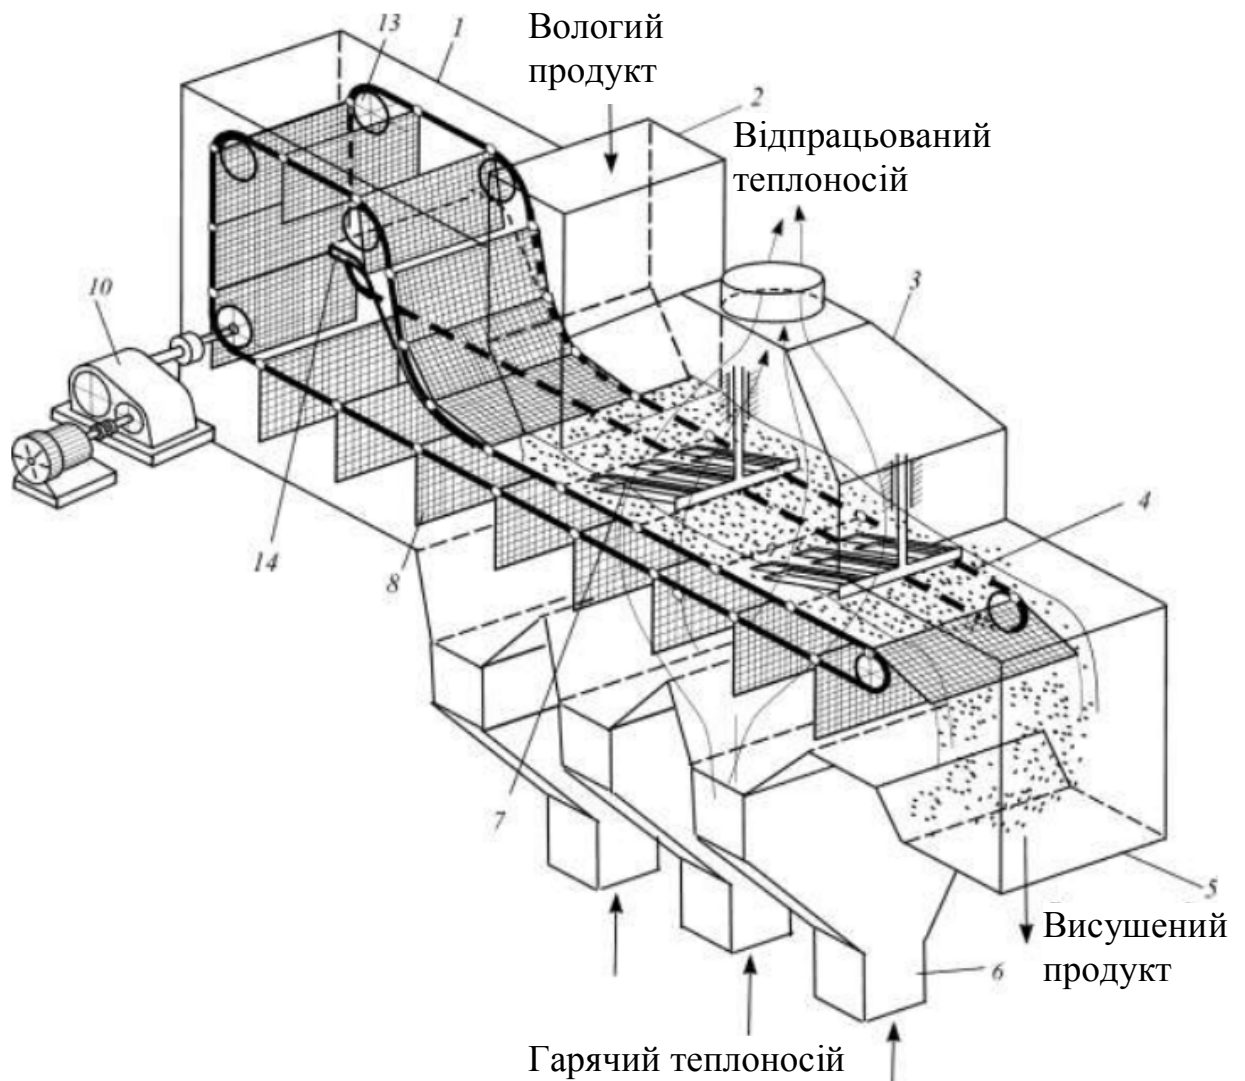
Сушарка: 1 - корпус; 2 - завантажувальний бункер; 3 - патрубок для відводу відпрацьованого сушильного агента; 4 - ланцюгові транспортери; 5 - розвантажувальний бункер; 6 - патрубки для підведення сушильного агента; 7 - гравітаційні перегрібачі; 8 - сітчасті пластини; 9 - верхня напрямна; 10 - регульований привід; 11 - пази; 12 - осі; 13 - ланцюгові зірочки; 14 - нижня напрямна; 15 - похилі лопатки; 16 - вирівнювач висоти; 17 - живильник
